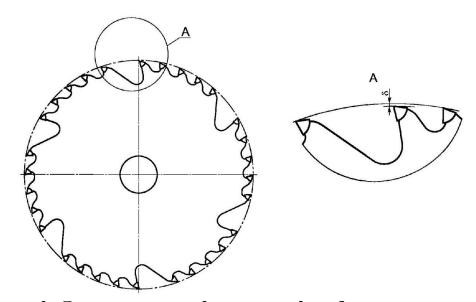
Дисковые пилы тип 2 исполнение 3 для бревнопильных станков
